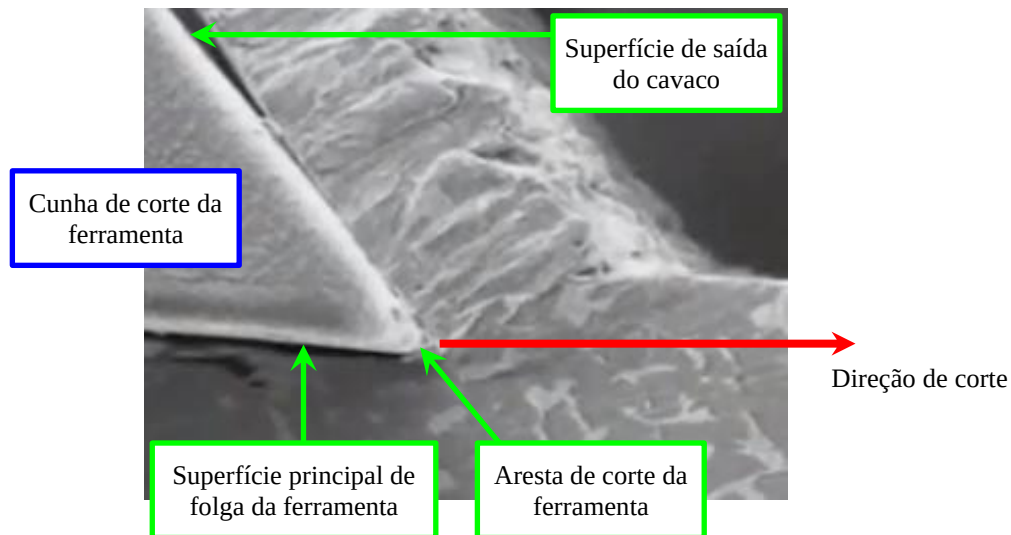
Ferramenta de usinagem em procedimento de corte de material: indicação da “superfície de saída do cavaco” e da “superfície principal de folga – entre a ferramenta de corte e o material sob usinagem”.
